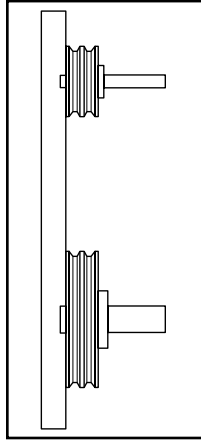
Zusammenbau der Antriebskomponenten mit geteiltem Gehäuse
